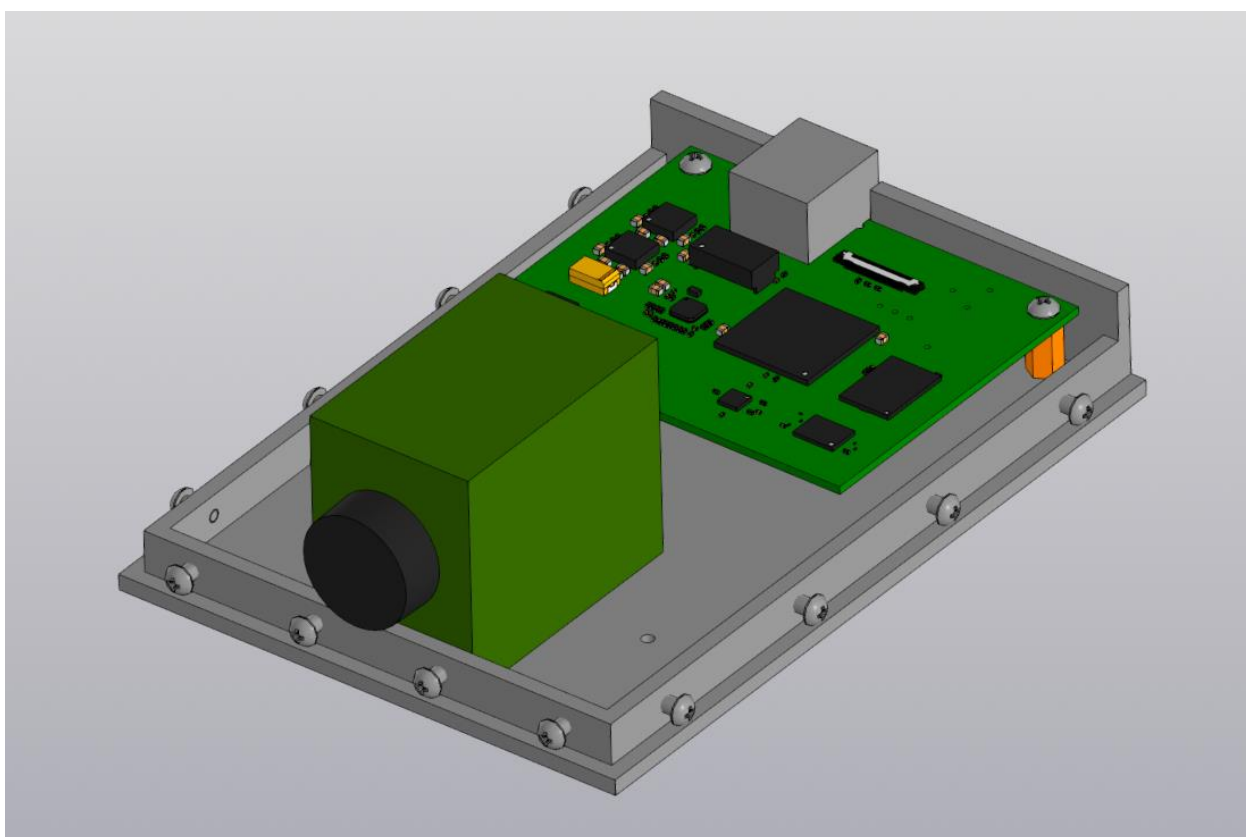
3D-изображение общей сборки: вид сверху спереди, без крышки, разъема питания и переключателя
